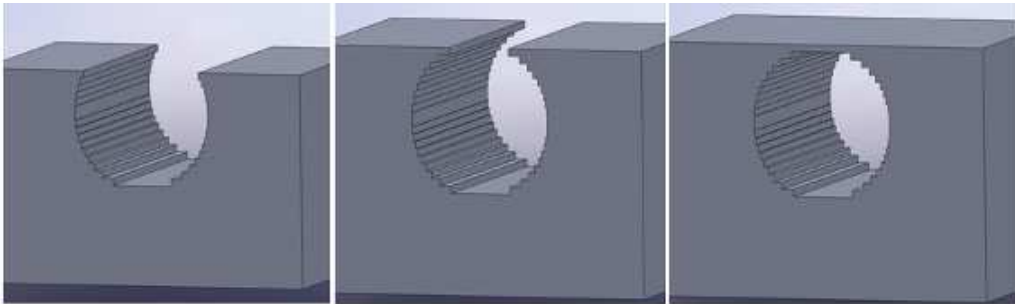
Diseño CAD 3D de un agujero cilíndrico horizontal.
